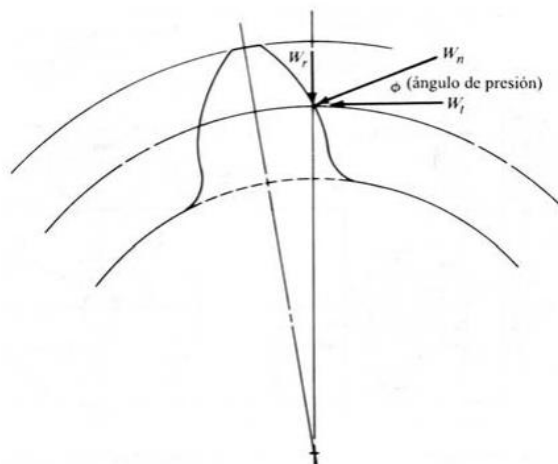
Ángulo de presión en un engranaje cilíndrico recto.
